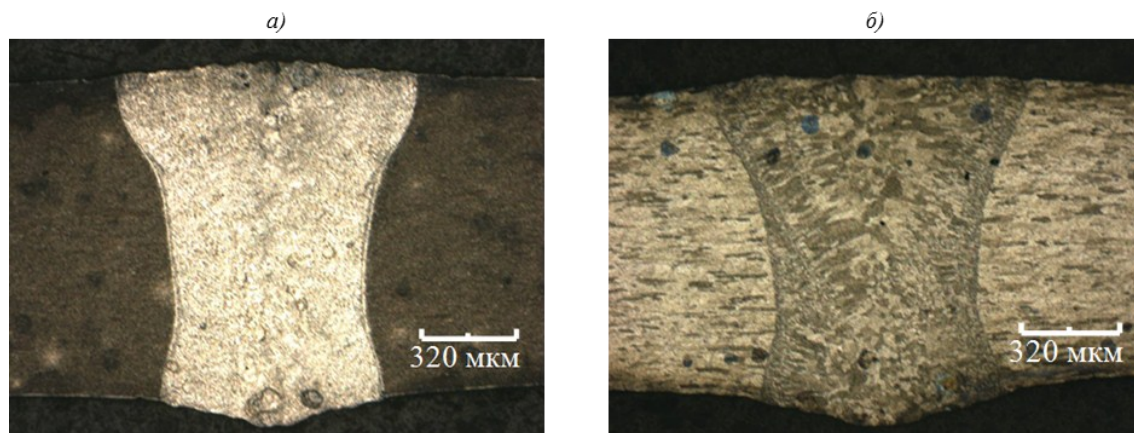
Макроструктура сварного соединения листов из сплава В-1469:
